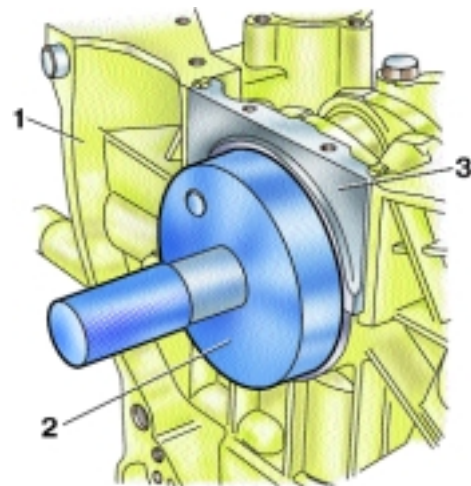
Установка оправки для запрессовки заднего сальника коленчатого вала двигателя F3R 272: 1 – блок цилиндров двигателя; 2 – оправка; 3 – крышка коренного подшипника 1-го цилиндра
